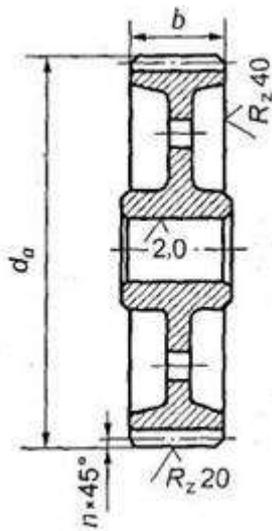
Эскиз цилиндрического прямозубого зубчатого колеса
